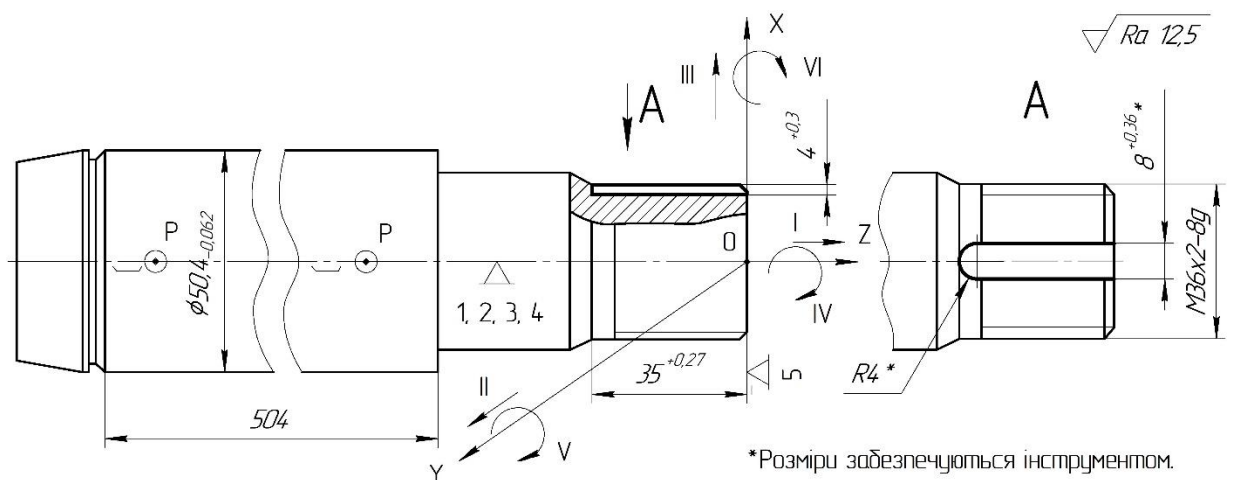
Ескіз заготовки на операції 030. Схема №2
